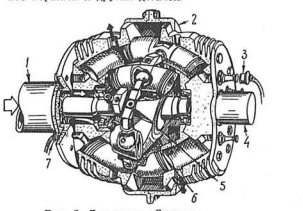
Двигатель «Селвуд» с кривошипно-шатунным валом. 1 — стационарный вал; 2 — кривошипно-шатунный вал; 3 — электрод высокого напряжения; 4 — радиатор; 5 — двойной шарнирный подшипник; 6 — крестовина; 7 — электрод высокого напряжения.
